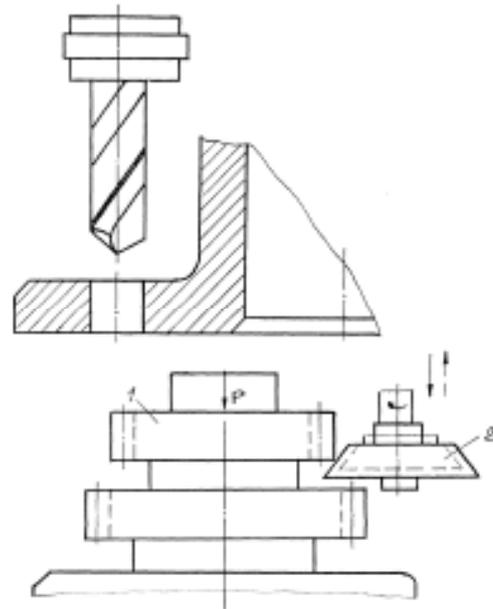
Конструкция детали, обеспечивающая удобный подвод режущего инструмента к обрабатываемой поверхности и свободный его выход после окончания обработки
